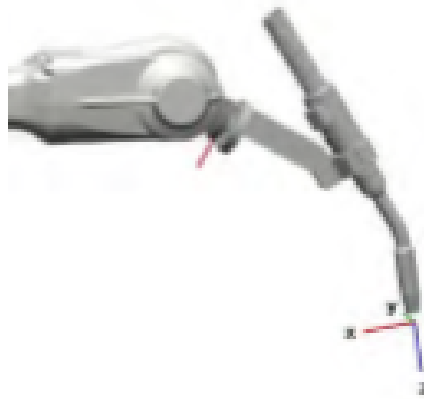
TCP de la herramienta Pistola de soldadura con Arco
